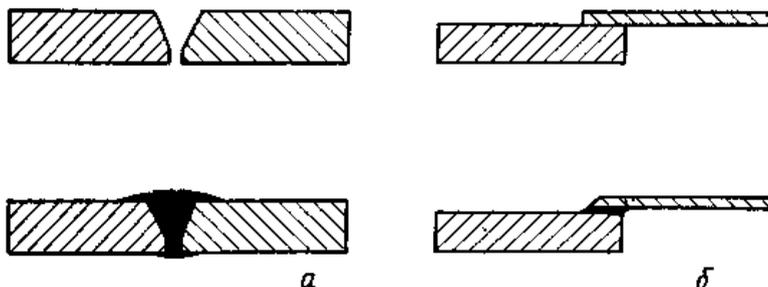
Схема образования шва при пайке-сварке:
